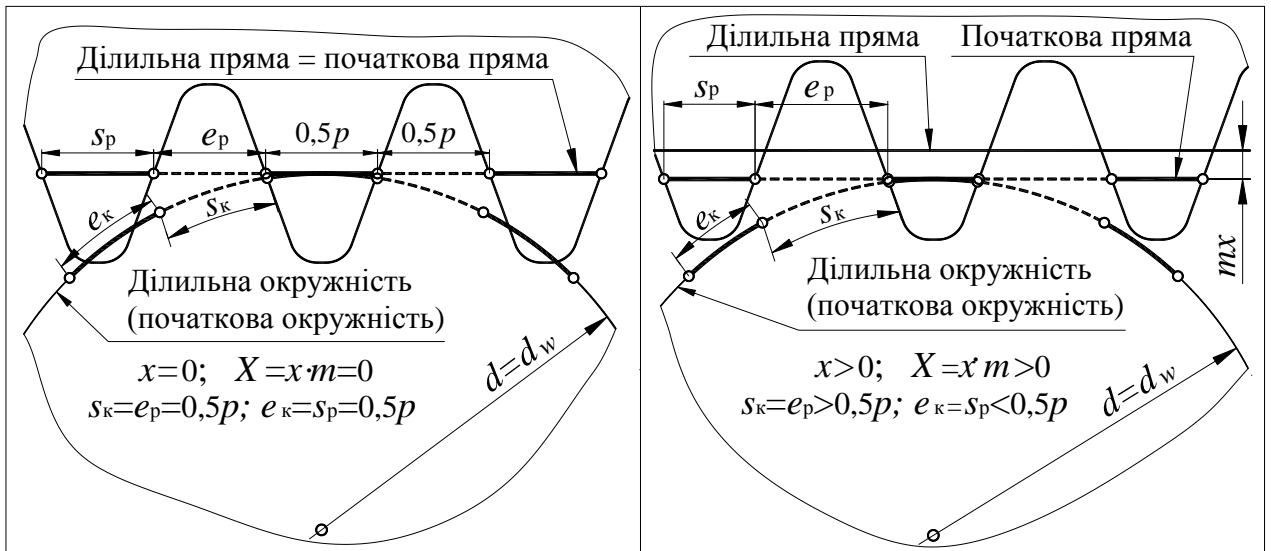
Нарізування зубчастих коліс із зсувом рейки
